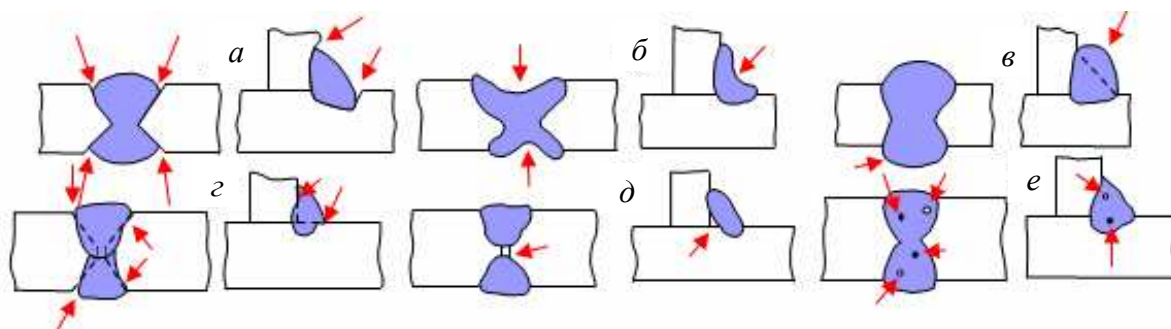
Дефекты сварных швов: *а* – подрезы, *б* – неполномерные швы, *в* – чрезмерное усиление валика, *г* – несплавление по кромке, *д* – непровары, *е* – шлаковые и газовые включения
